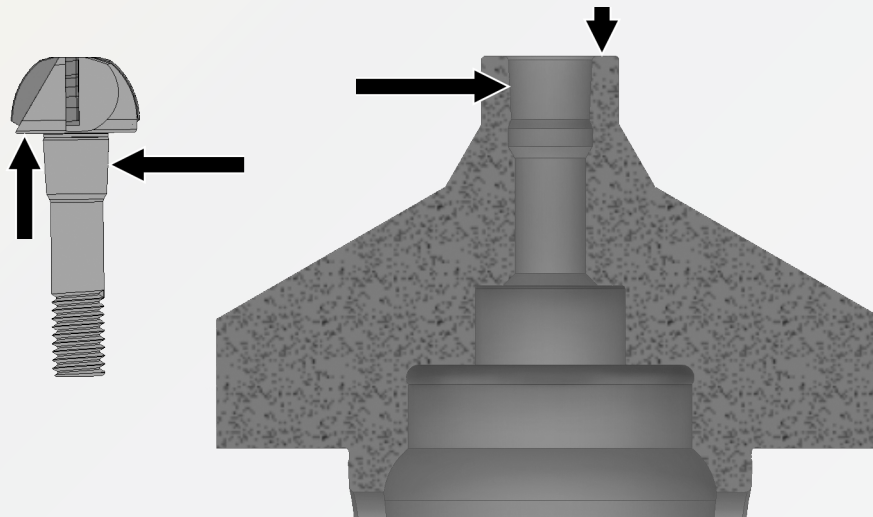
Kugelbahnfräser (Inner Race) reinigen
